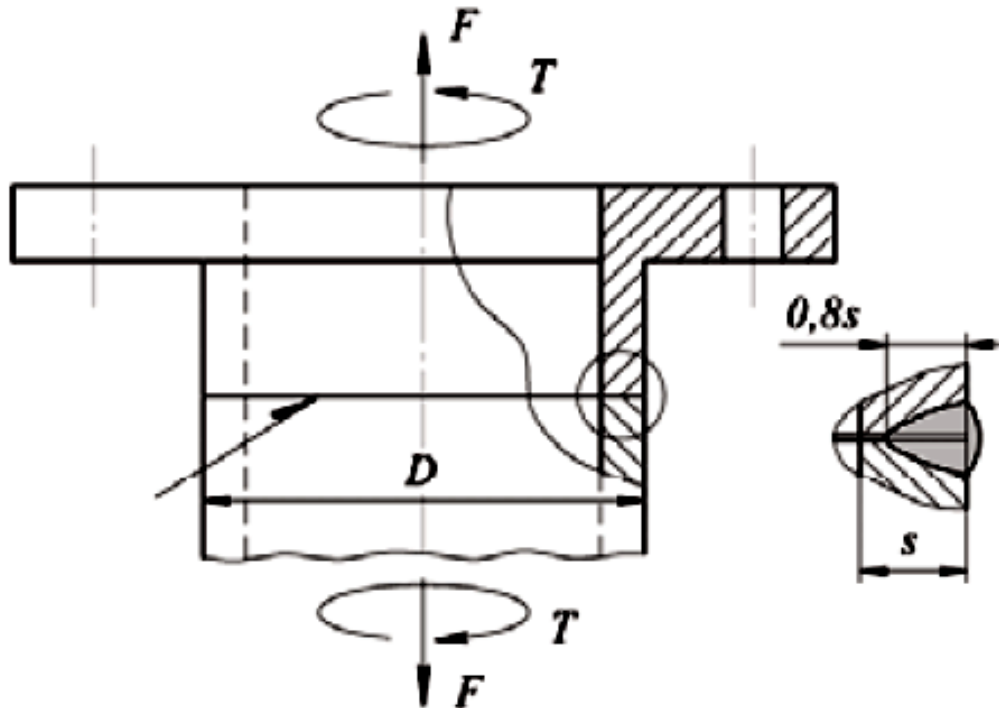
Сварное соединение встык трубы и фланца штанги буровой установки
